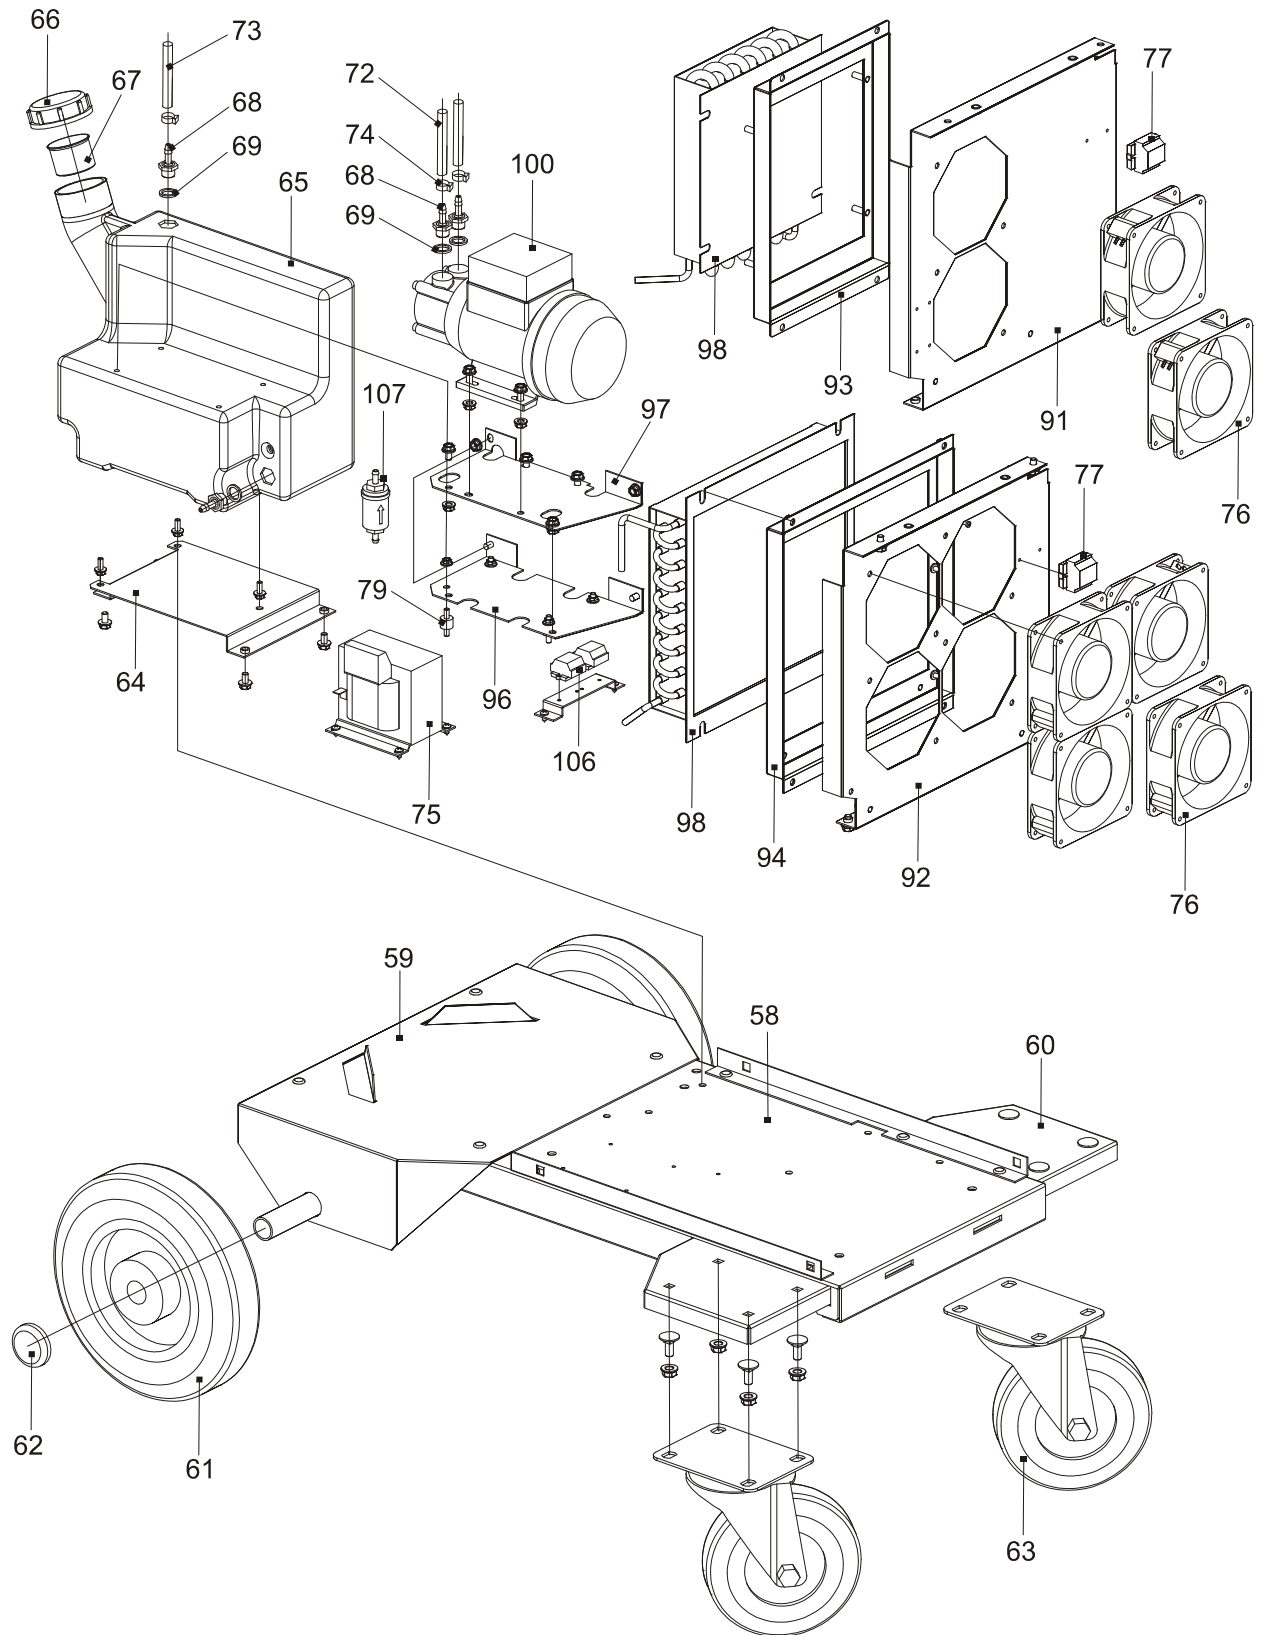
Explosionszeichnung INVERTIG.PRO COMPACT,
